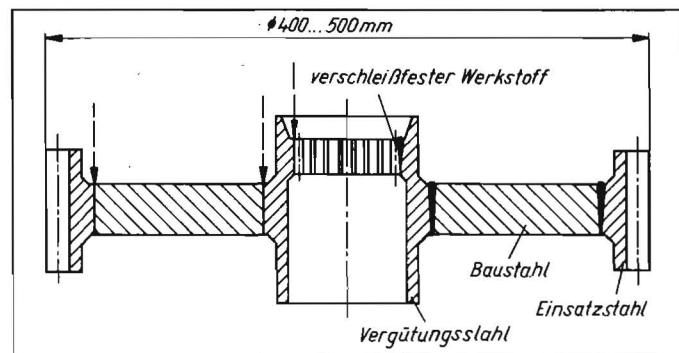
Aufgeschweißte Zahnäder auf einer Getriebewelle
